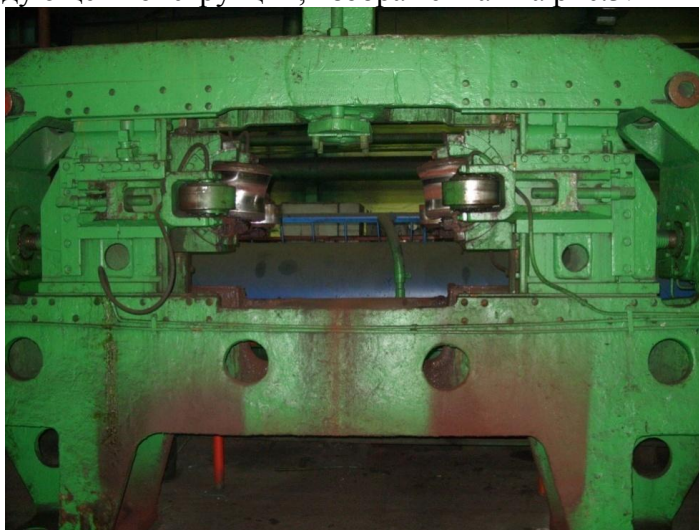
Кромкогибочная клетя конструкции ЭЗТМ
